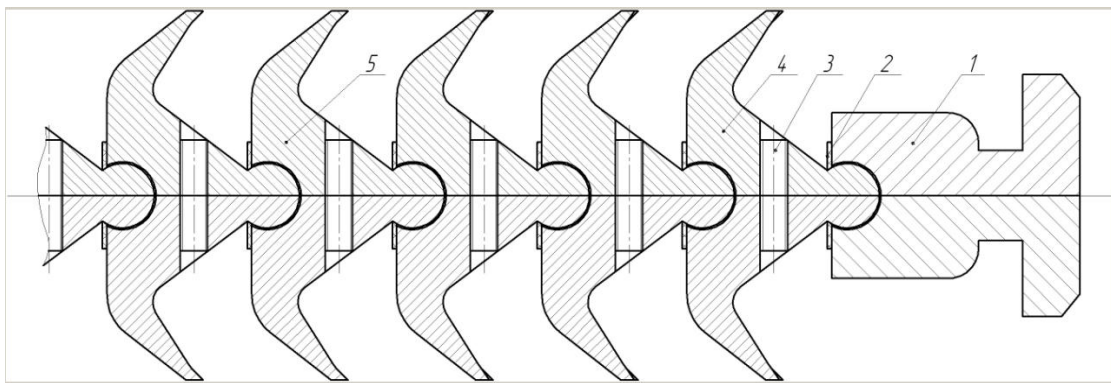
Конструкція гнучкої протяжки для оброблення отворів
